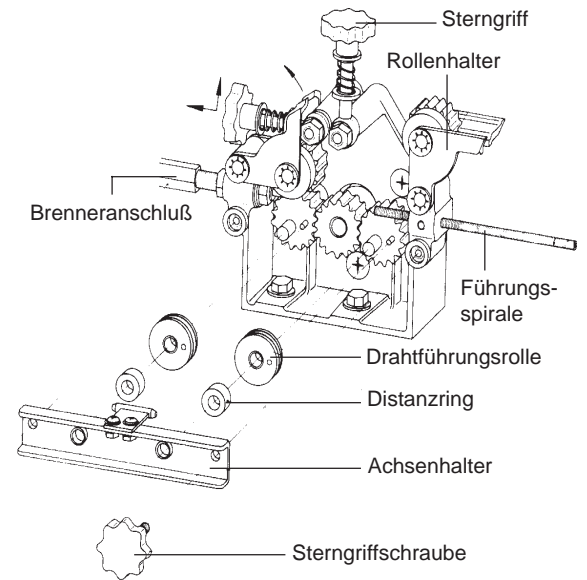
Geöffneter Drahtvorschub mit Explosionszeichnung
